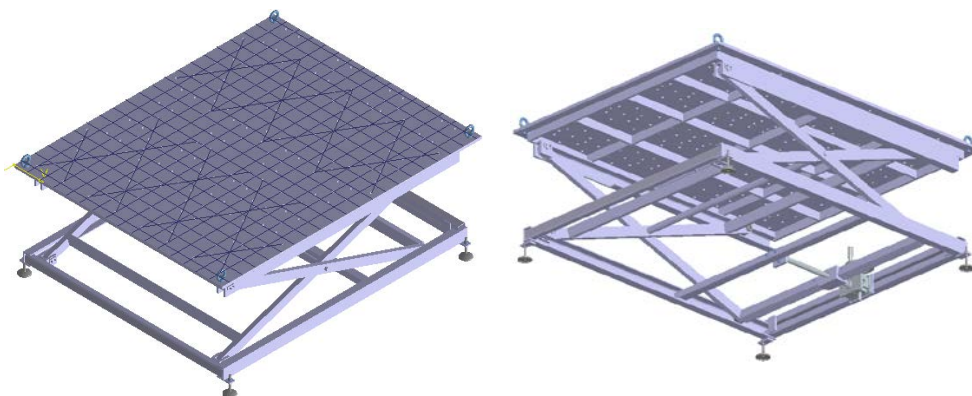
Modelo definitivo de la mesa de soldadura
